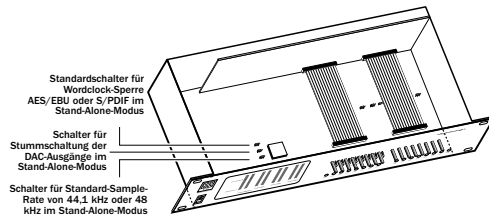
Position des Jumper-Schalters im 888/24 I/O
